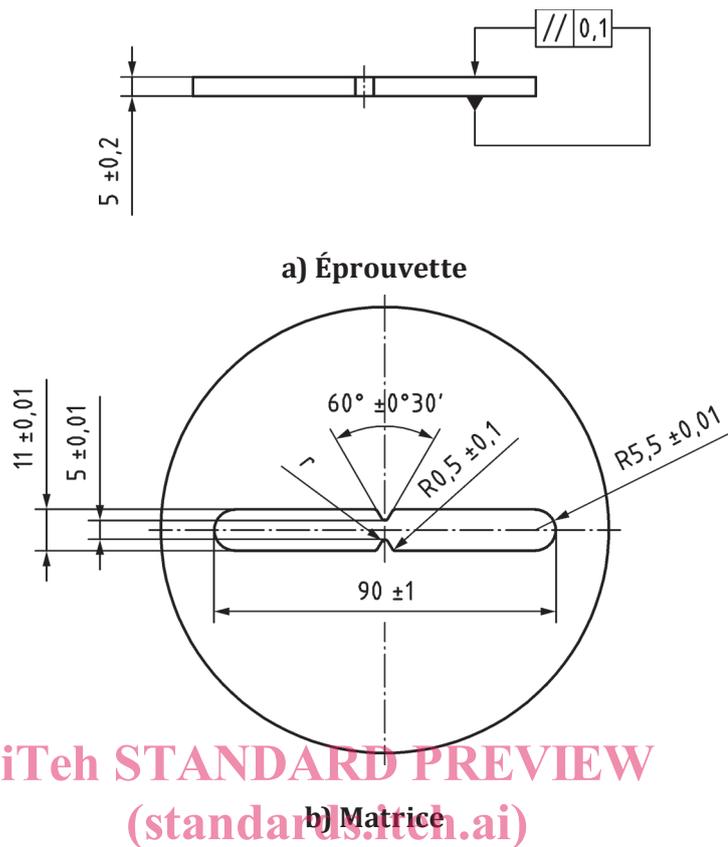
Éprouvette entaillée et matrice de compression utilisée pour former des éprouvettes entaillées destinées à des essais de fatigue
